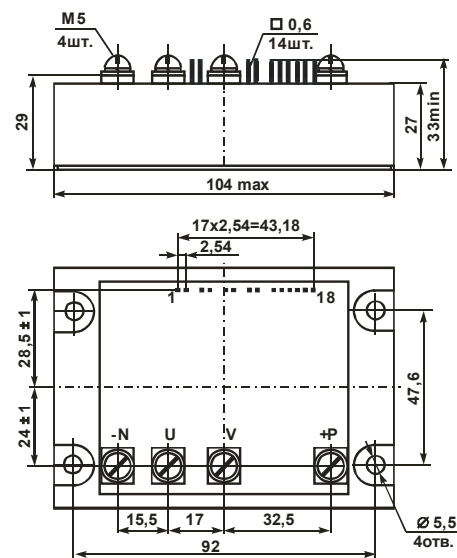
Габаритный чертеж модулей M13B-30(50,90)-6(12)
